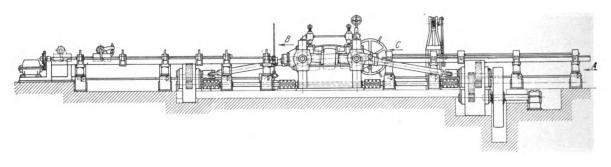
Schweres Friemelwalzwerk für Werkzeugstahl bis 160 mm Durchmesser.
